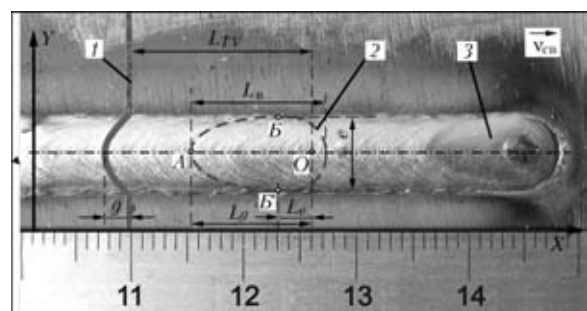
Схема возникновения транспортных запаздываний между сварочной ванной и ЛТС при сварке МАГ: 1 — световой след ЛТС; 2 — воображаемый контур сварочной ванны; 3 — поверхность затвердевшей сварочной ванны
